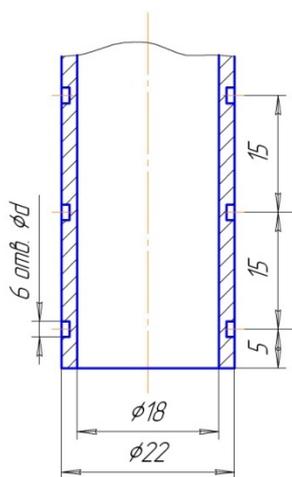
Экспериментальное сопло сварочной горелки
